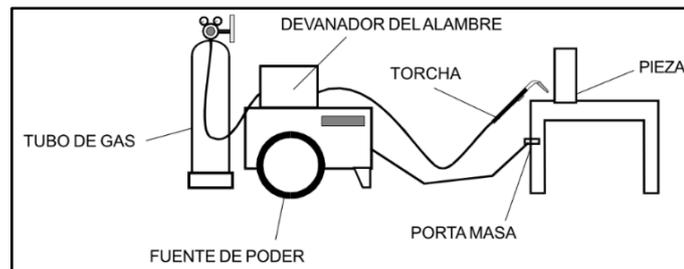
Esquema del proceso de soldadura MIG utilizado
